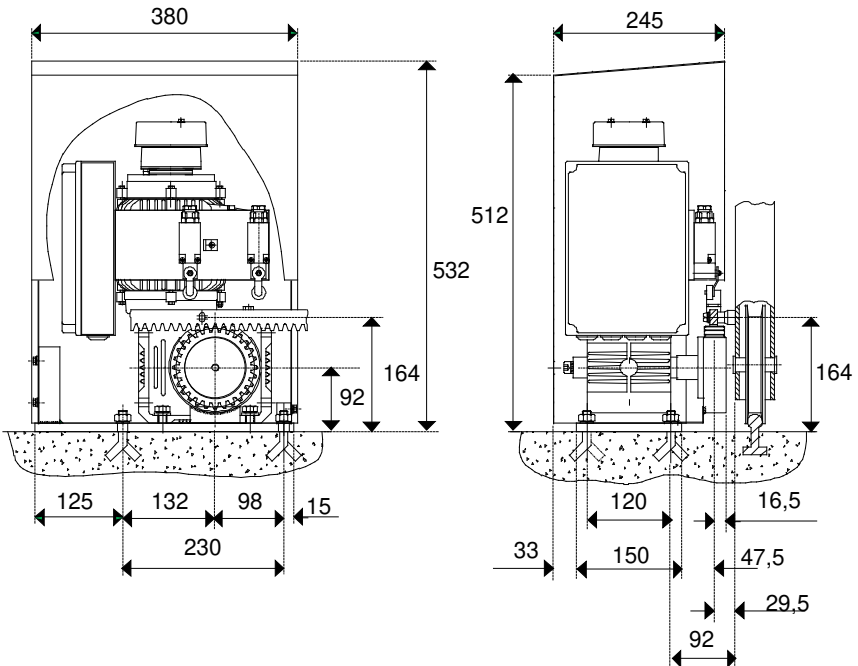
Maßbild der Type DS 1200 mit Zahnstange und Zahnrad
